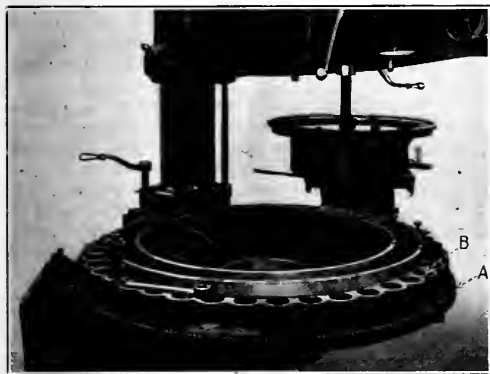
PIEZA QUE VA A SER TALADRADA DEL TALADRO
